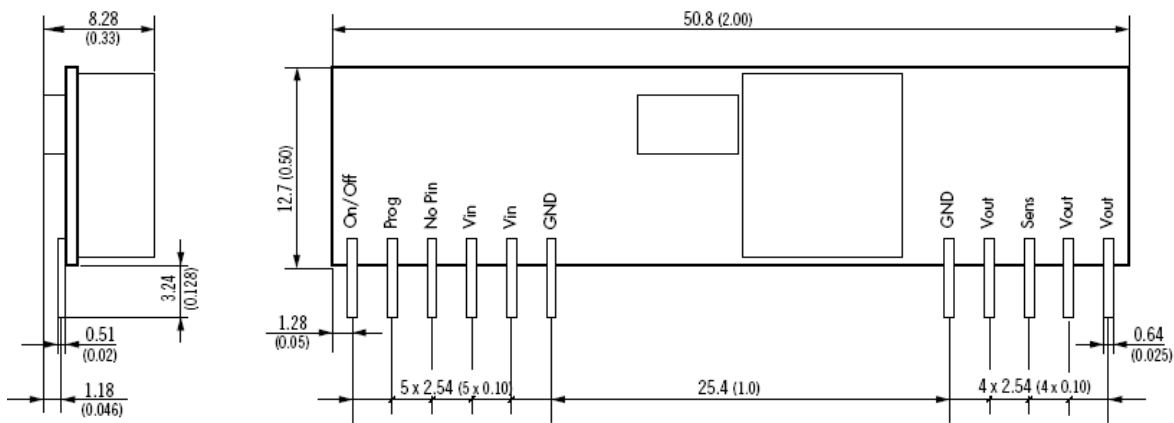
Чертеж корпуса моделей TOS 10-05SIL, TOS 10-12SIL, TOS 16-05SIL, TOS 16-12SIL
